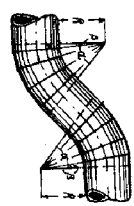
Сварная утка, состоящая из шести звеньев и четырех стаканов.
